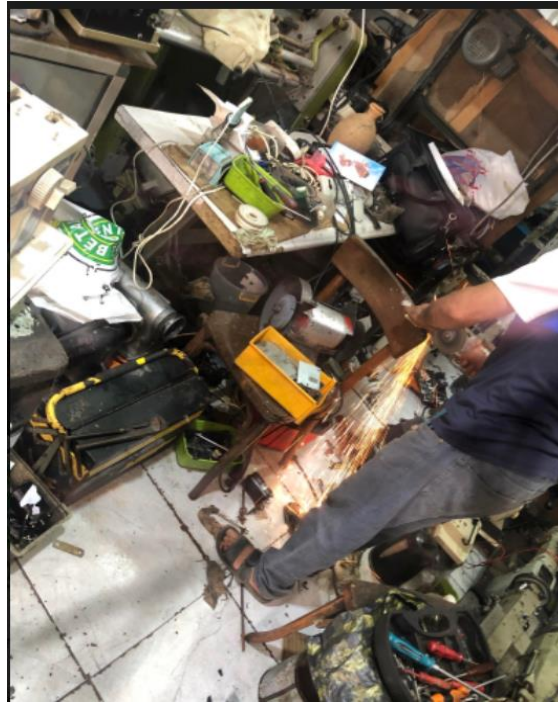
1.Modification sur la machine à coudre chez le réparateur
